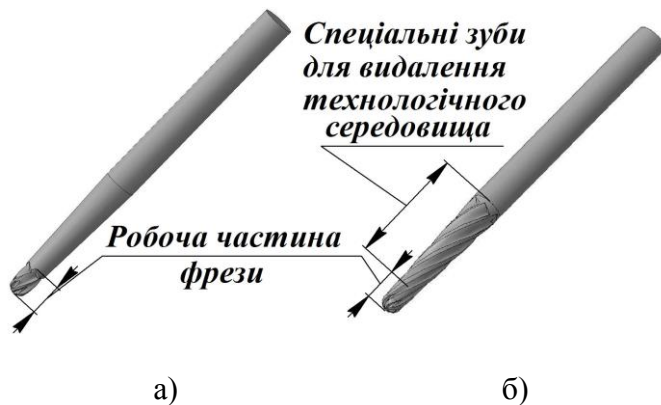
Конструкція фрези: а – традиційна кінцева фреза; б - кінцева фреза зі спеціальними зубами, призначеними для видалення надлишків технологічного середовища
